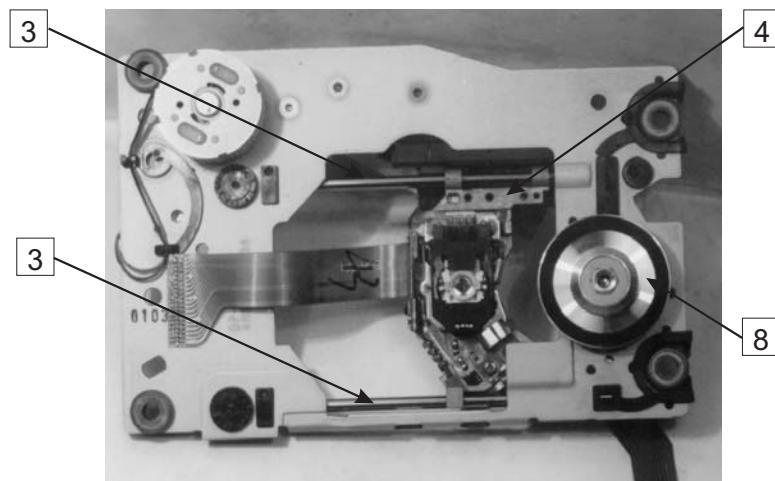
Внешний вид механизма привода дисков. Вид сверху
